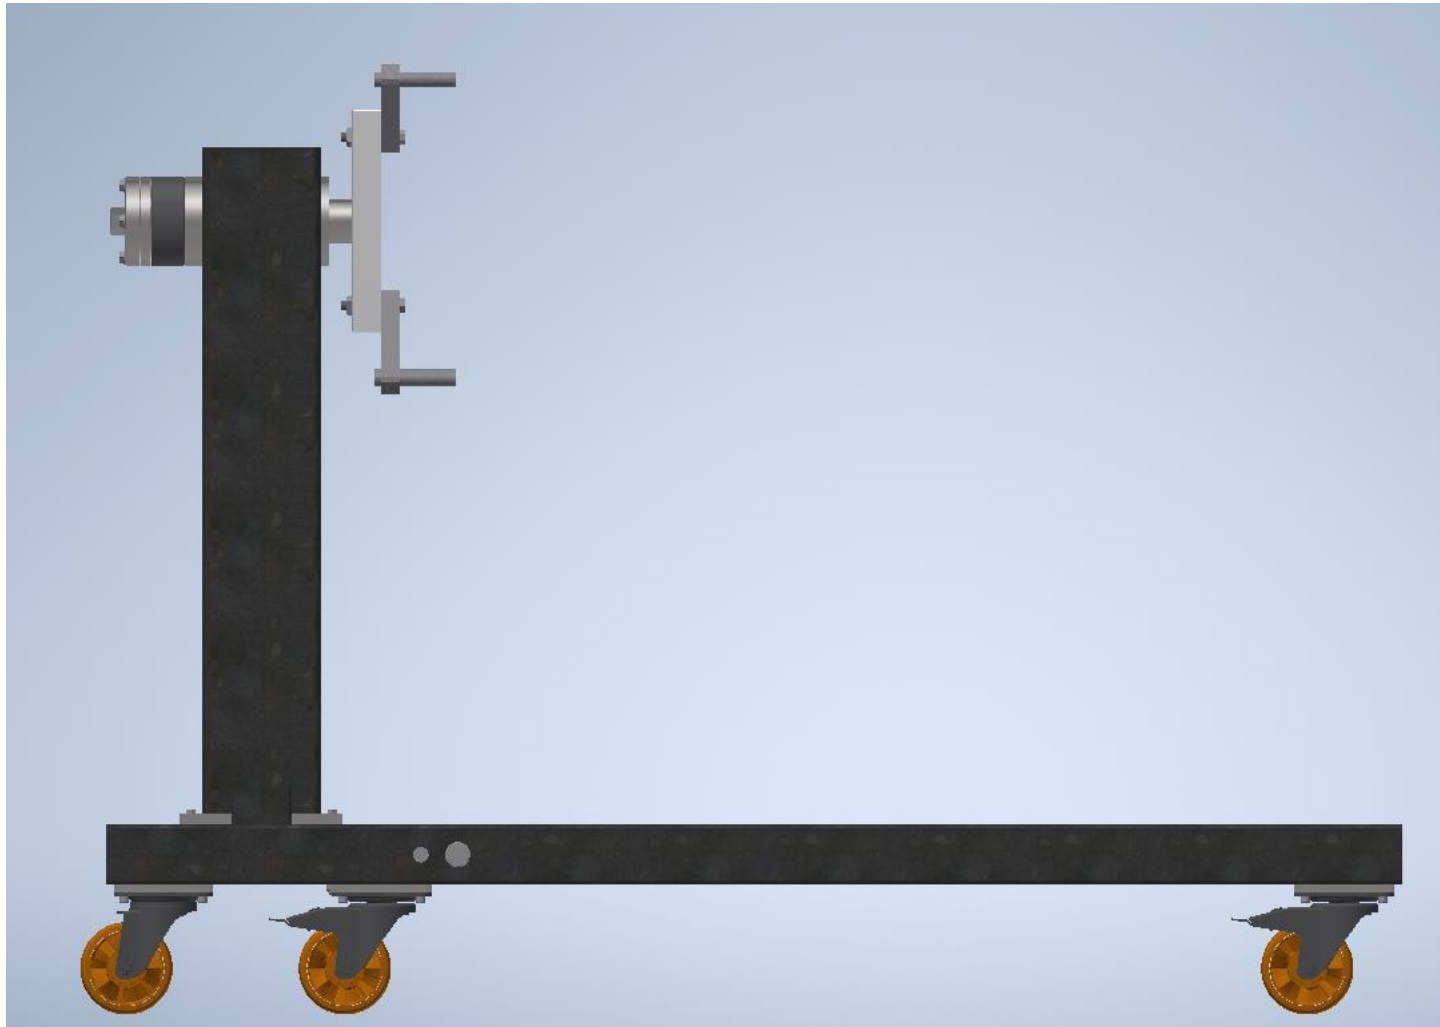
Motor-Montagevorrichtung Seitenansicht
